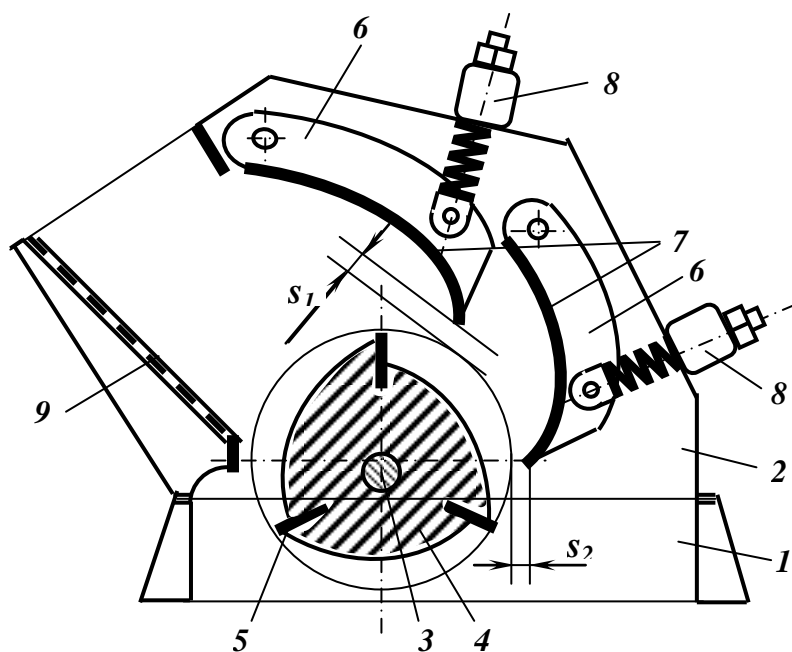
Однороторна дробарка крупного дроблення.
